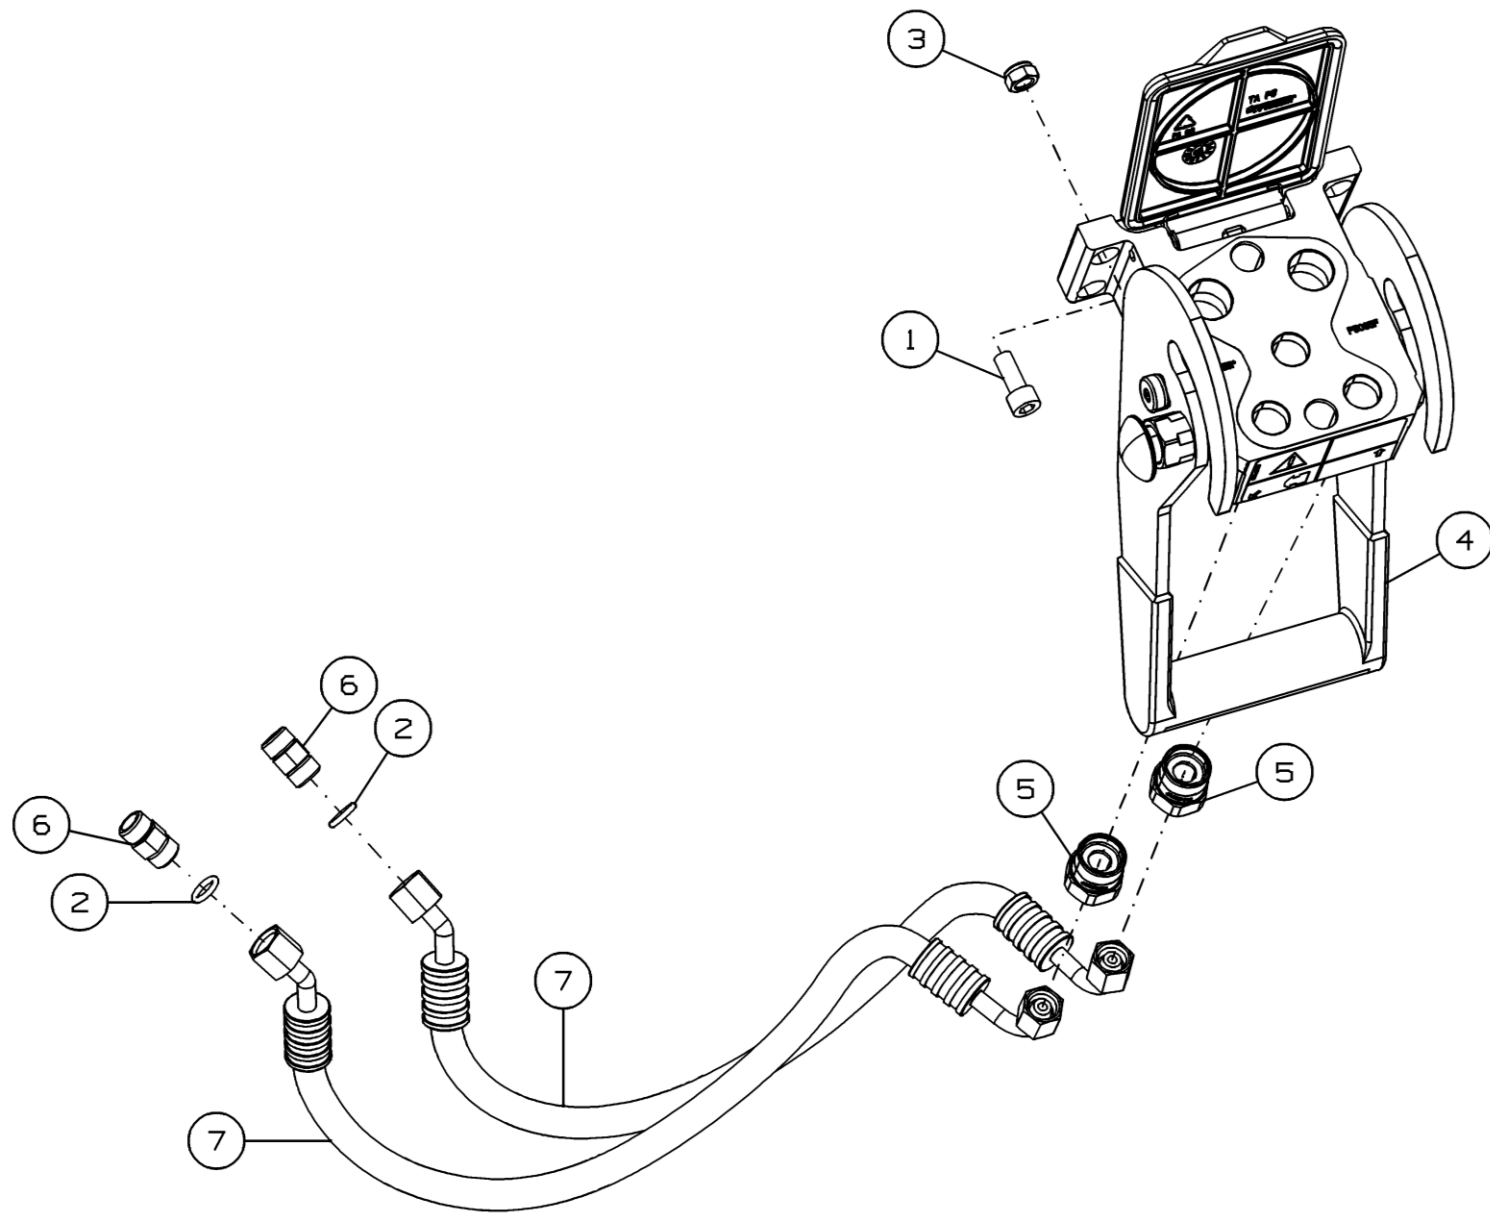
Установка единого гидроразъема FASTER ППК-870.15.00.000А
